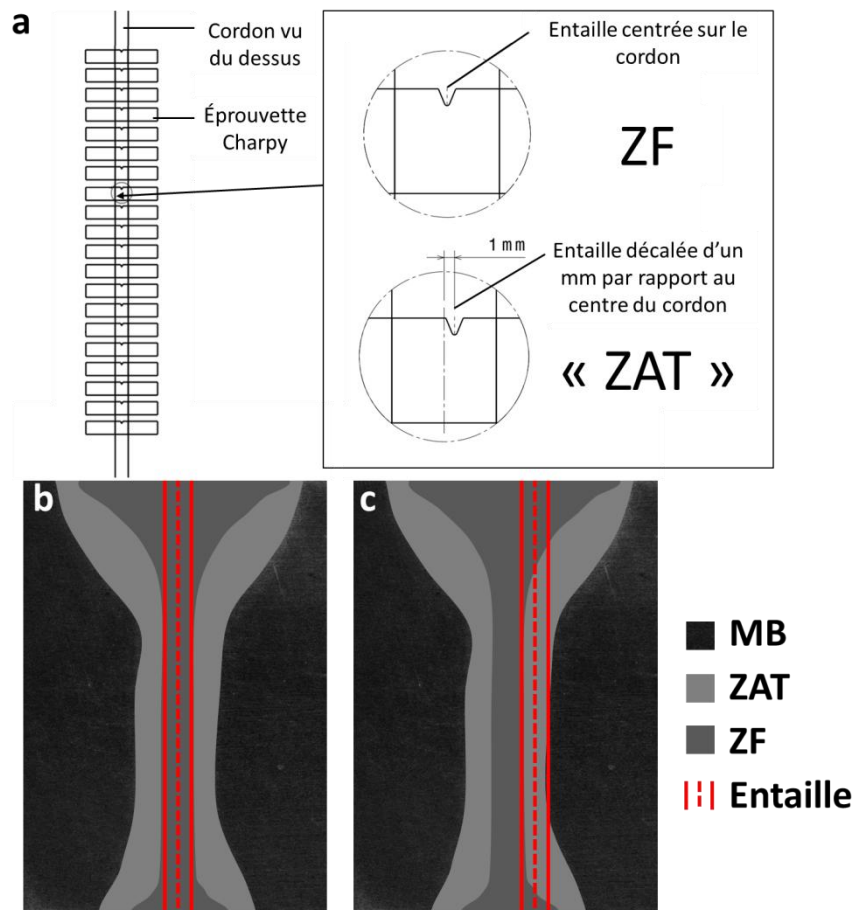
Prélèvement des éprouvettes vue de dessus (a) et vue de coupe de l'emplacement de l'entaille en V pour les éprouvettes Charpy de type ZF (a) et « ZAT » (b)
